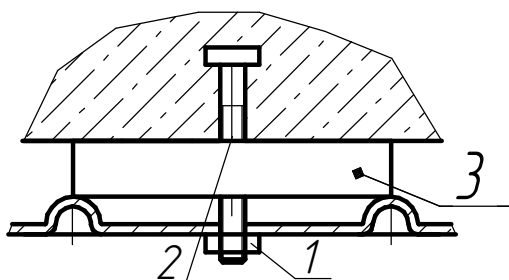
1 - корпус в сборе; 2 - крышка; 3 - рассеиватель.
